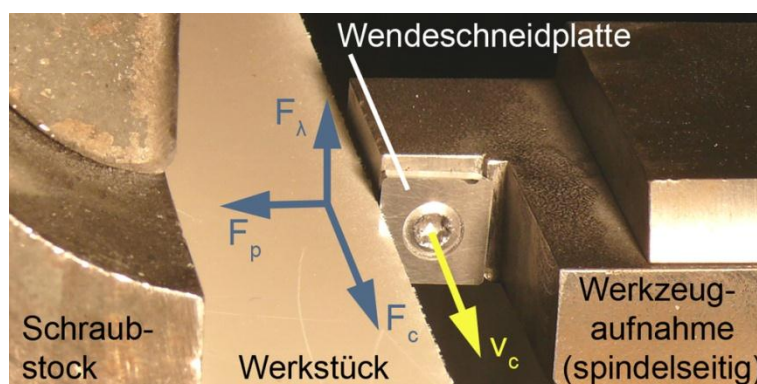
Versuchsaufbau des Stoßprozesses: Werkzeug im Eingriff; während des Schnitts gemessene Kraftkomponenten
